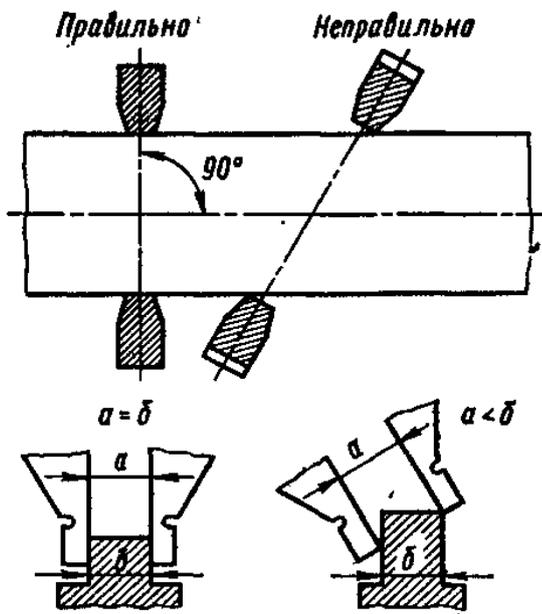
Установка штангенциркуля при измерении наружных поверхностей
